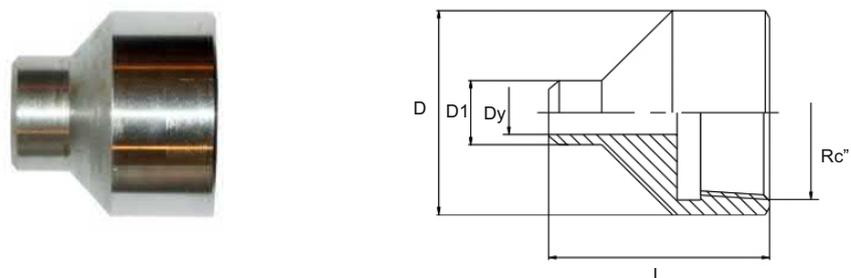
Муфта переходная для соединения РВД с трубопроводом
